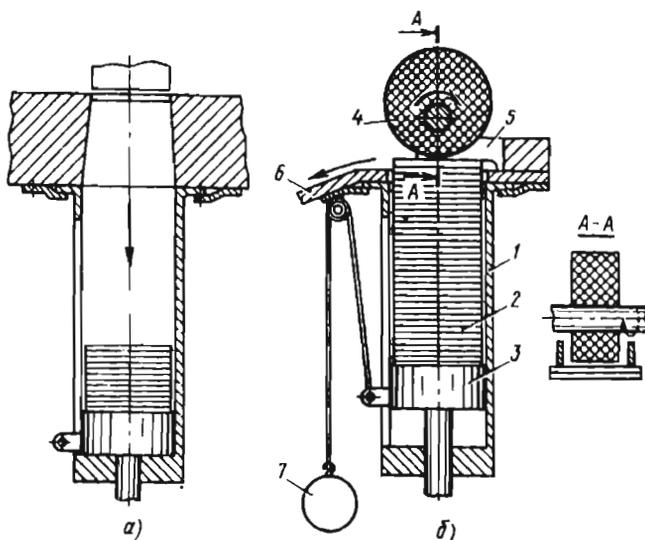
Пример магазинного питания с предварительным штапелированием заготовок:
